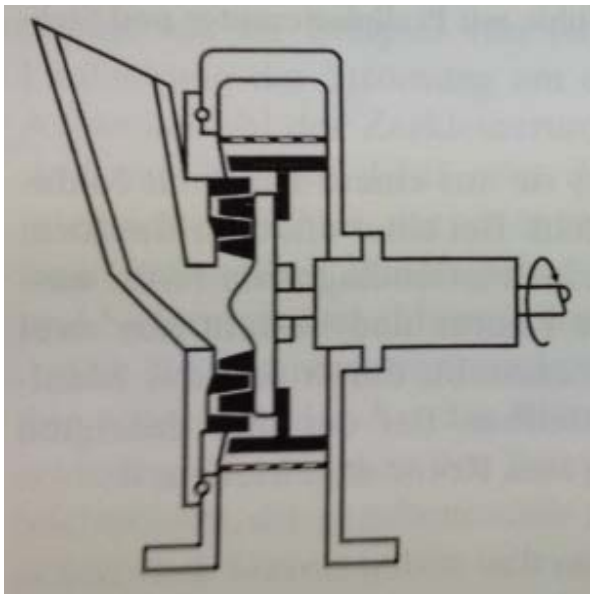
Mühle mit Nockenrotor und Siebklassierung (42)
